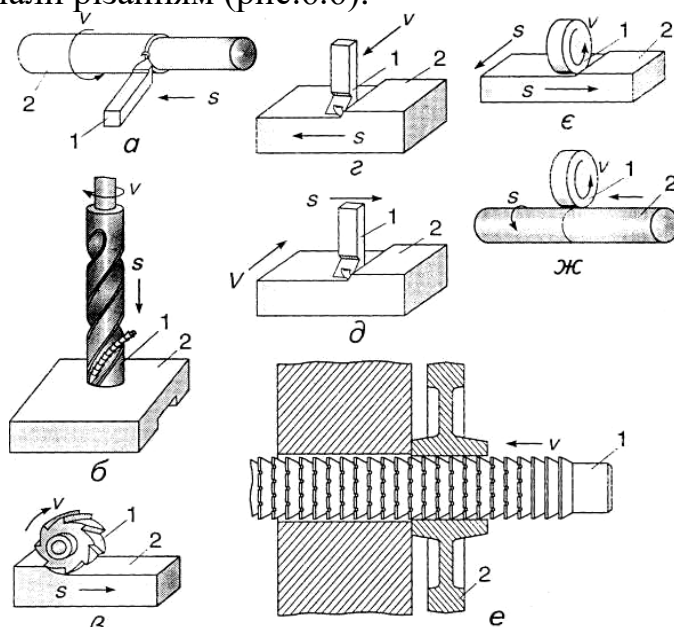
Види обробки різанням: а – точіння; б – свердління; в – фрезерування; г – поперечне стругання; д – поздовжнє стругання; е – протягування; є – плоске шліфування; ж – кругле шліфування; 1 – різальний інструмент; 2 – заготовка.
